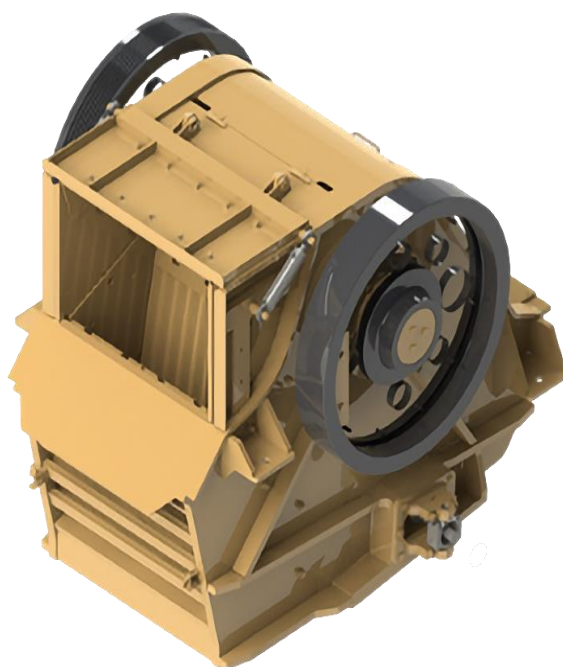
Загальний вигляд дробарки DCJ 1038
